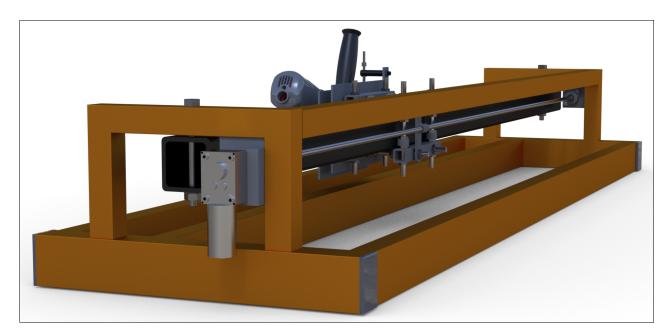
Vista lateral derecho. Fuente: elaboración propia.
